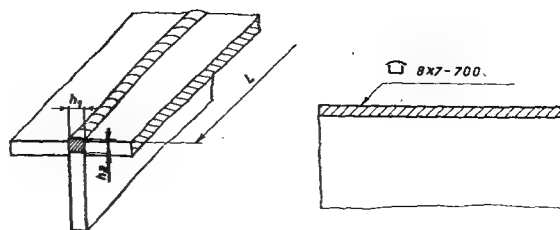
Ejemplo de representación unificada de soldadura sobre tres chapas con $h_1 = 8$ mm; $h_2 = 7$ mm; $L = 700$ mm.
